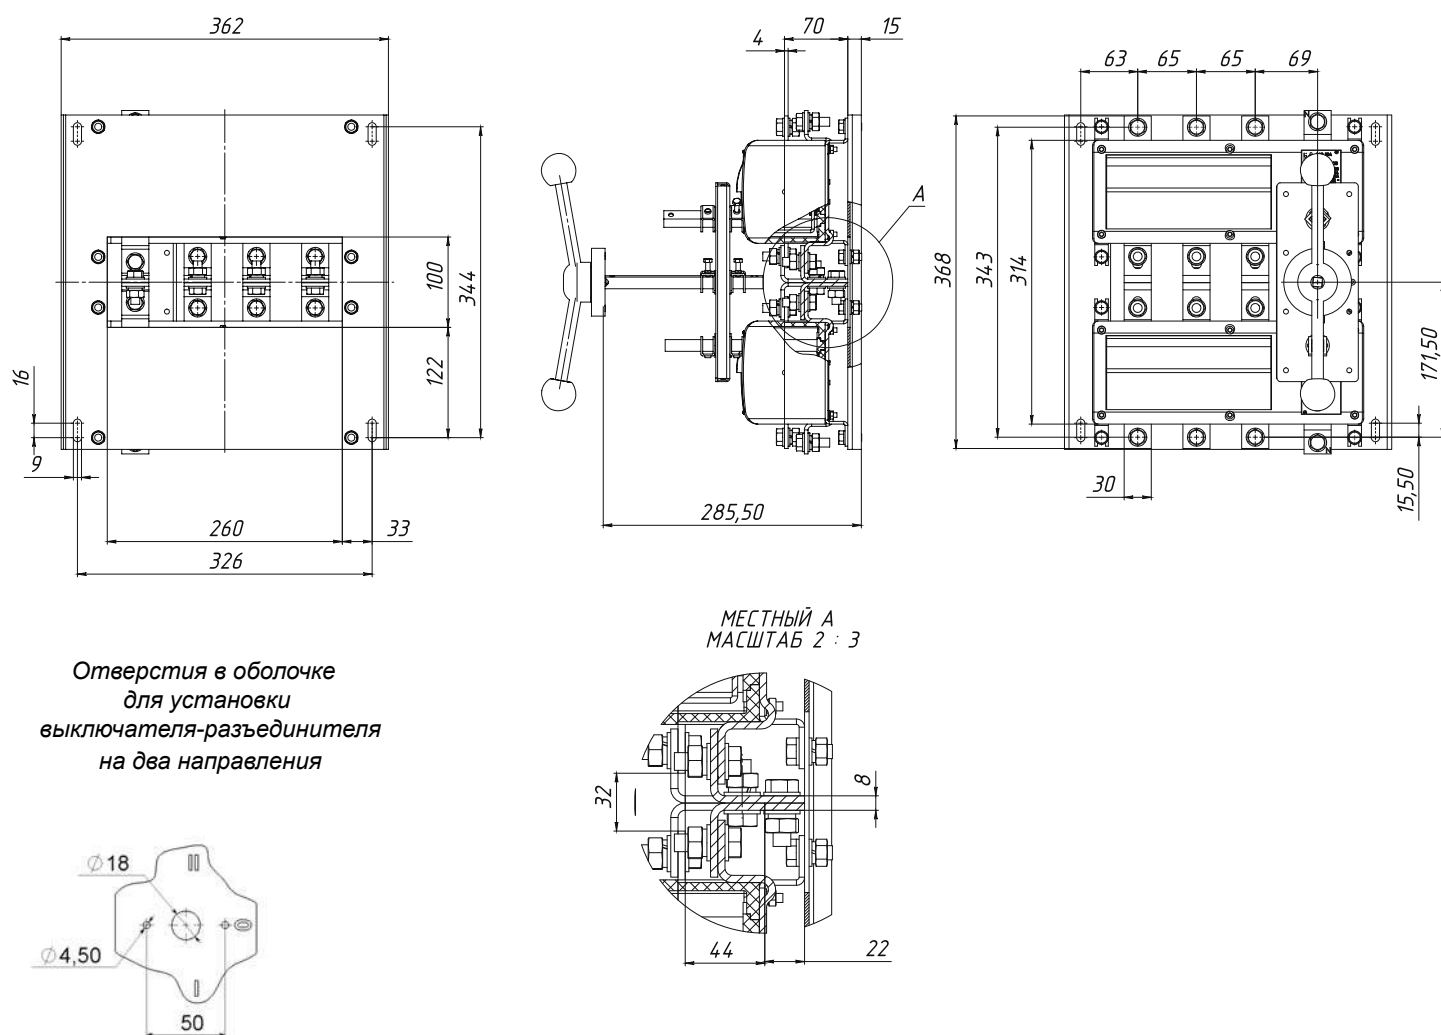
Выключатель-разъединитель ВНК-35-71130-32 УХЛ3 на два направления, масса не более – 11,9 кг
